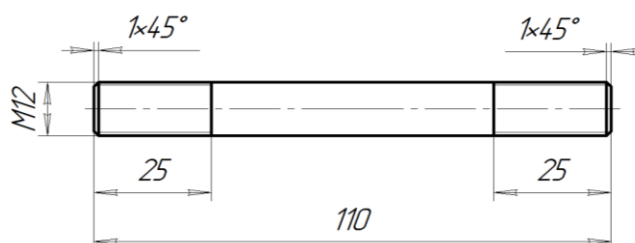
Чертеж шпильки с одинаковыми резьбовыми концами
